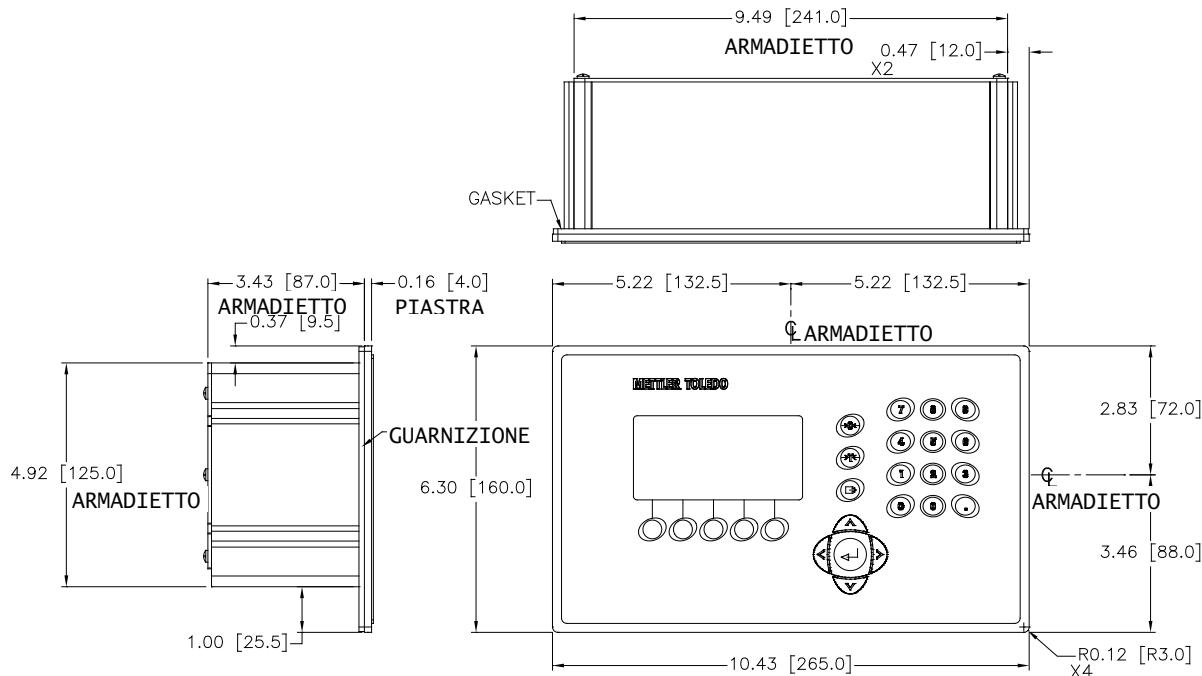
Dimensioni del montaggio a pannello dell'IND560
